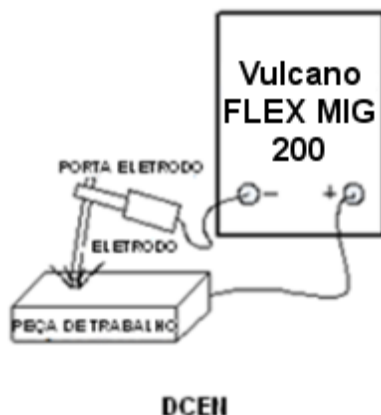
Conexão negativa para soldagem com eletrodo revestido
